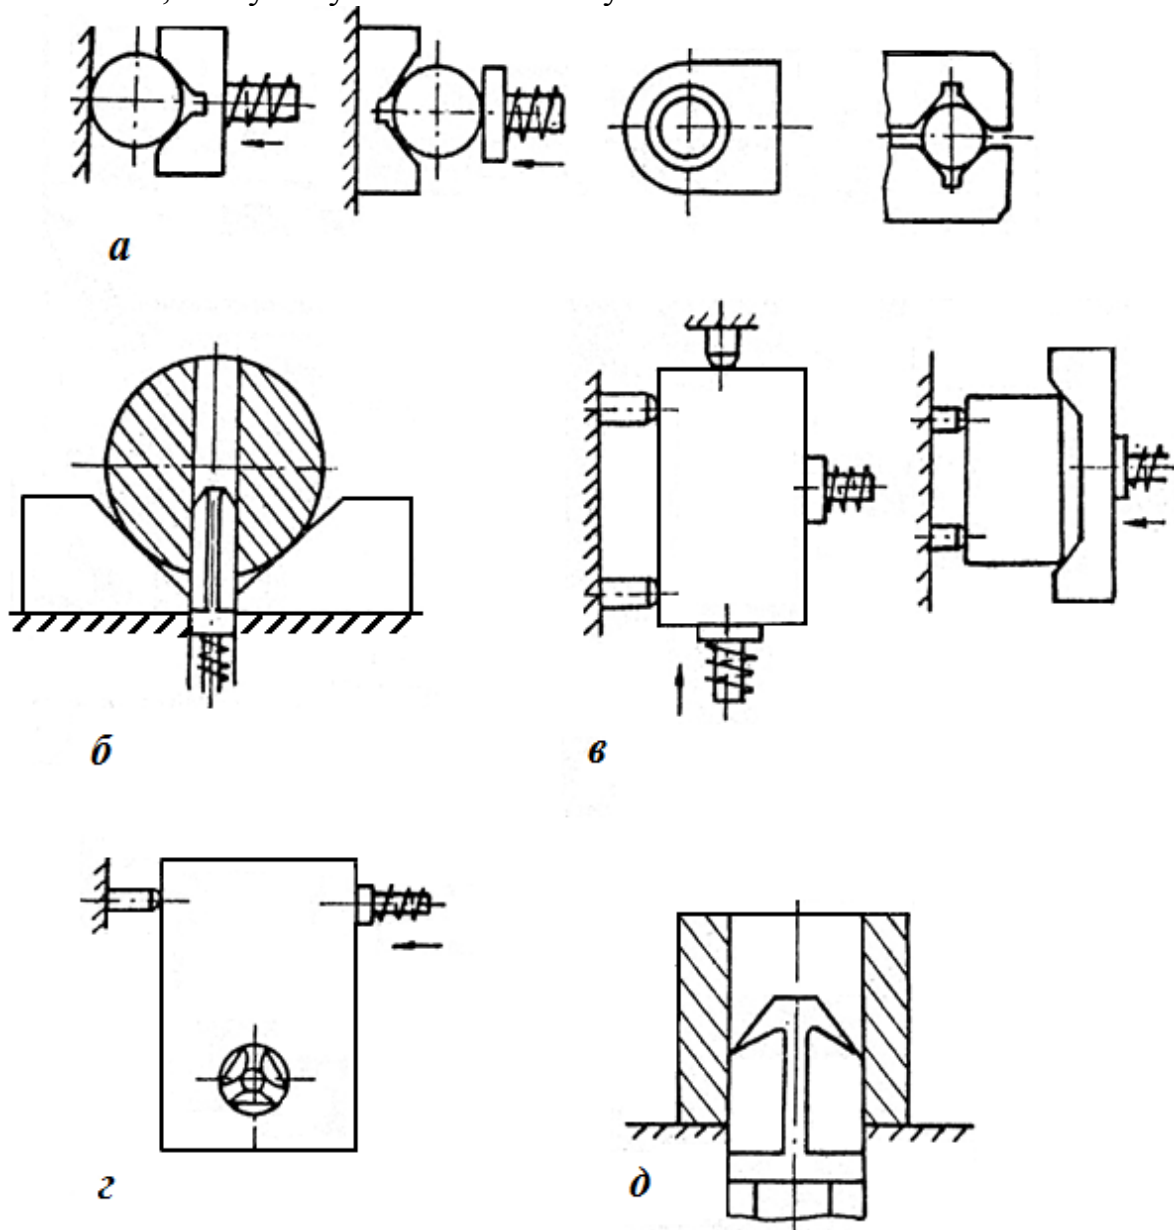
Схеми базування деталей на позиції складання: а - вала; б - вала з отвором; в - пластины; г - пластины з отвором; д - втулки
